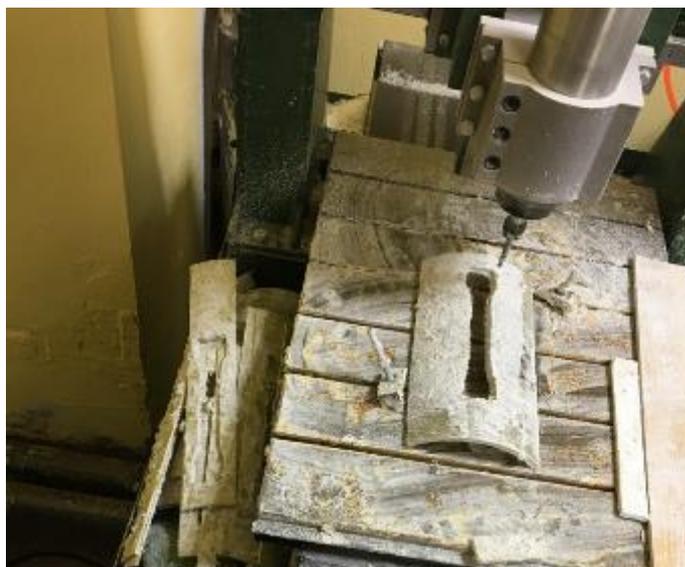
Процесс изготовления образцов на фрезерном станке
